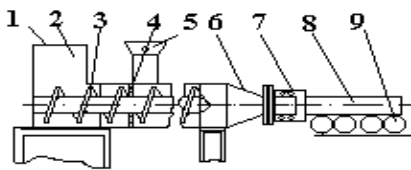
Схема экструдера: 1 – пресс; 2 – загрузочная камера; 3 – вал; 4 – решетка; 5 – вакуум-камера; 6 – головка пресса; 7 – мундштук; 8 – изделия; 9 – ролик
